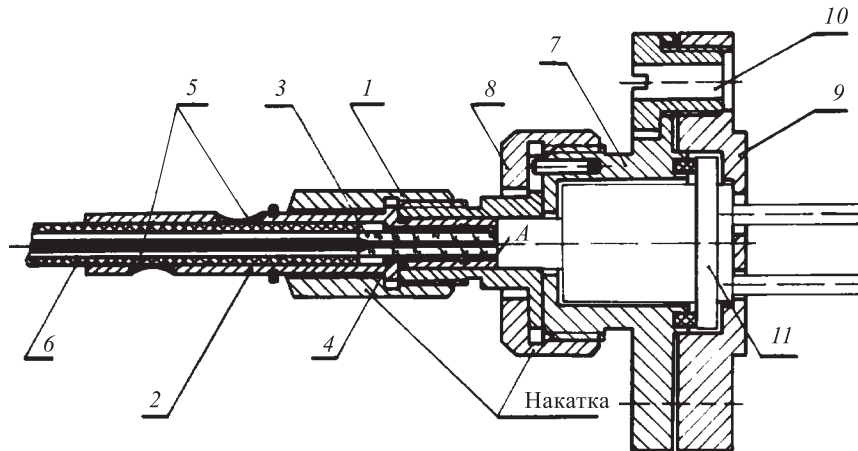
Универсальный юстируемый разъемный соединитель: 1 — вилка; 2 — хвостовик; 3 — стеклянный капилляр; 4, 5 — полость; 6 — оболочка волоконно-оптического световода; 7 — розетка; 8 — гайка (фиксатор); 9 — основание; 10 — отверстие для крепления; 11 — компоненты ВОЛС: суперлюминесцентный светодиод или фотодиод
